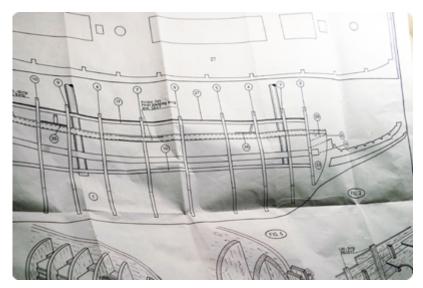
Schiffsrumpfunterbau. Lage der Spanten, Unterdecks und Kanonengerüste
